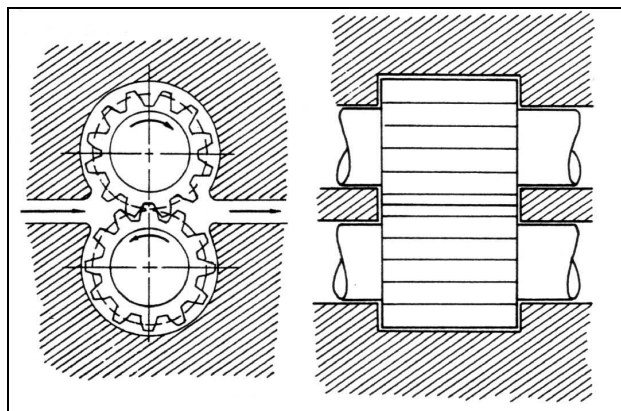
Dos vistas de la bomba de engranajes . (Throne 596)
